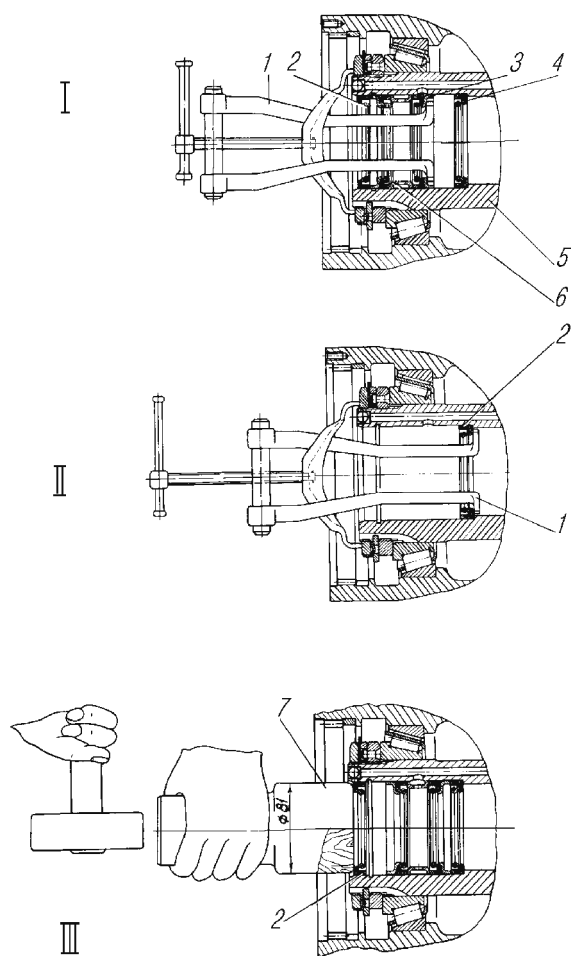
Демонтаж (I, II) и установка (III) деталей блока манжет подвода воздуха:
